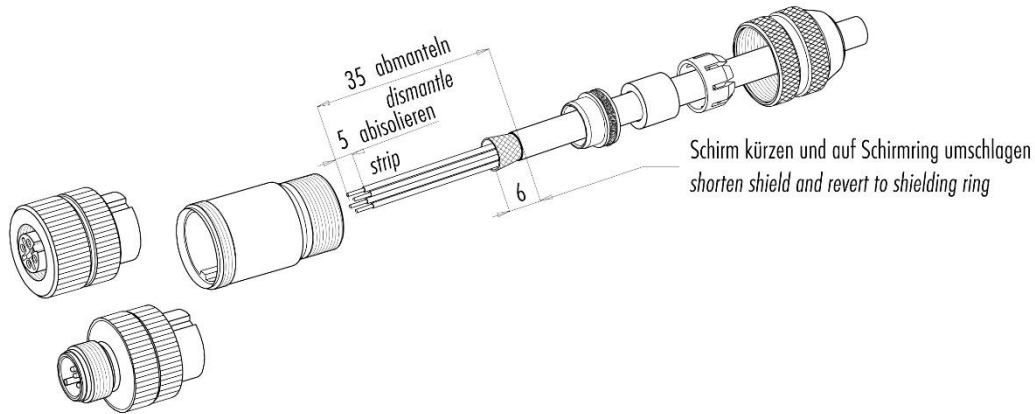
Montageanleitung für geschirmte Steckverbinder M12
